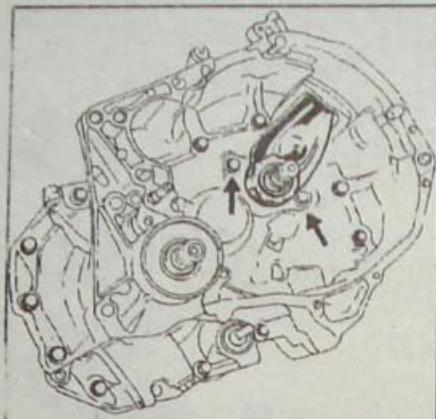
Расположение болтов крепления направляющей втулки подшипника выключения сцепления
